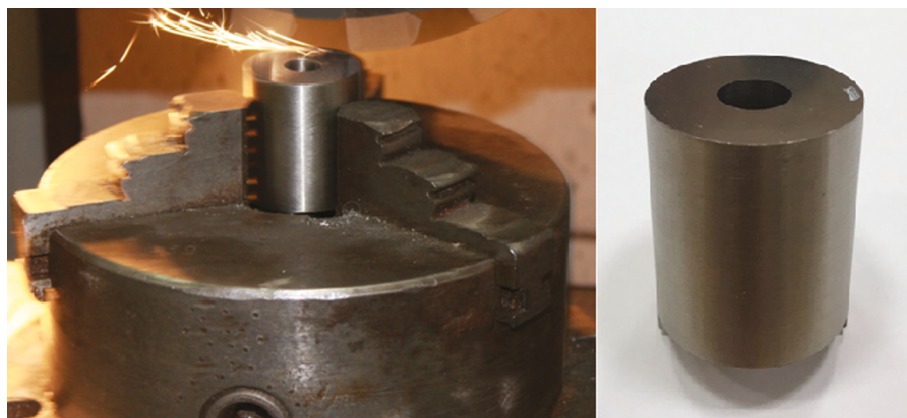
Процесс обработки заготовки из титана ВТ-6
